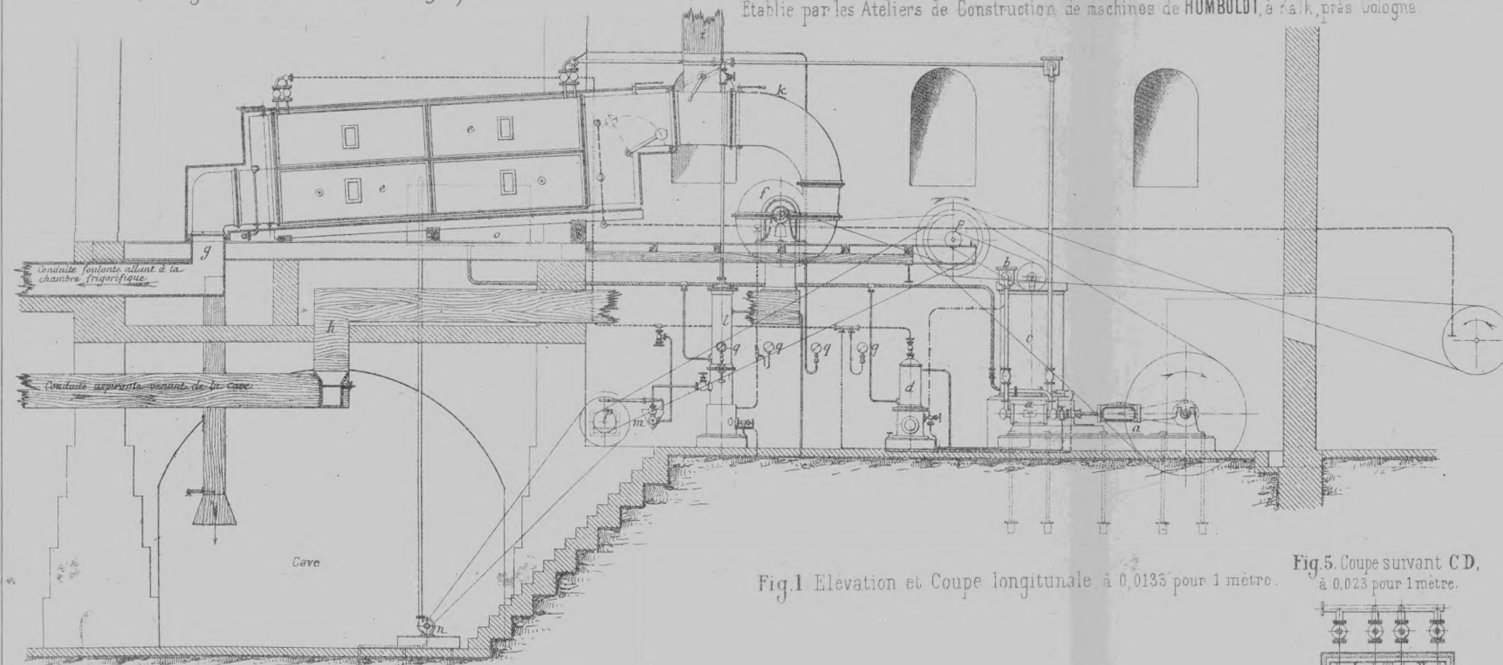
Elevation et Coupe longitudinale à 0,0133 pour 1 mètre.
